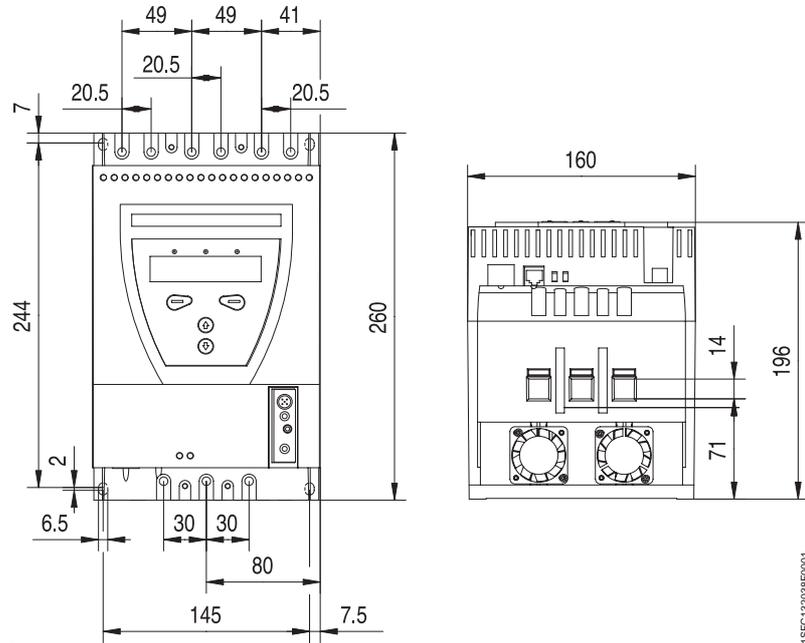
Dimensions PST30...72 (mm) (1 mm = 0,0394 pouce)
